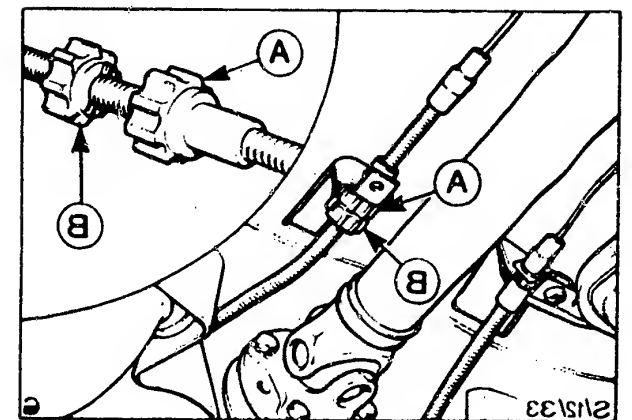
Das Einstellen des Handbremskabels: A Einstellmutter – B Kontermutter.
